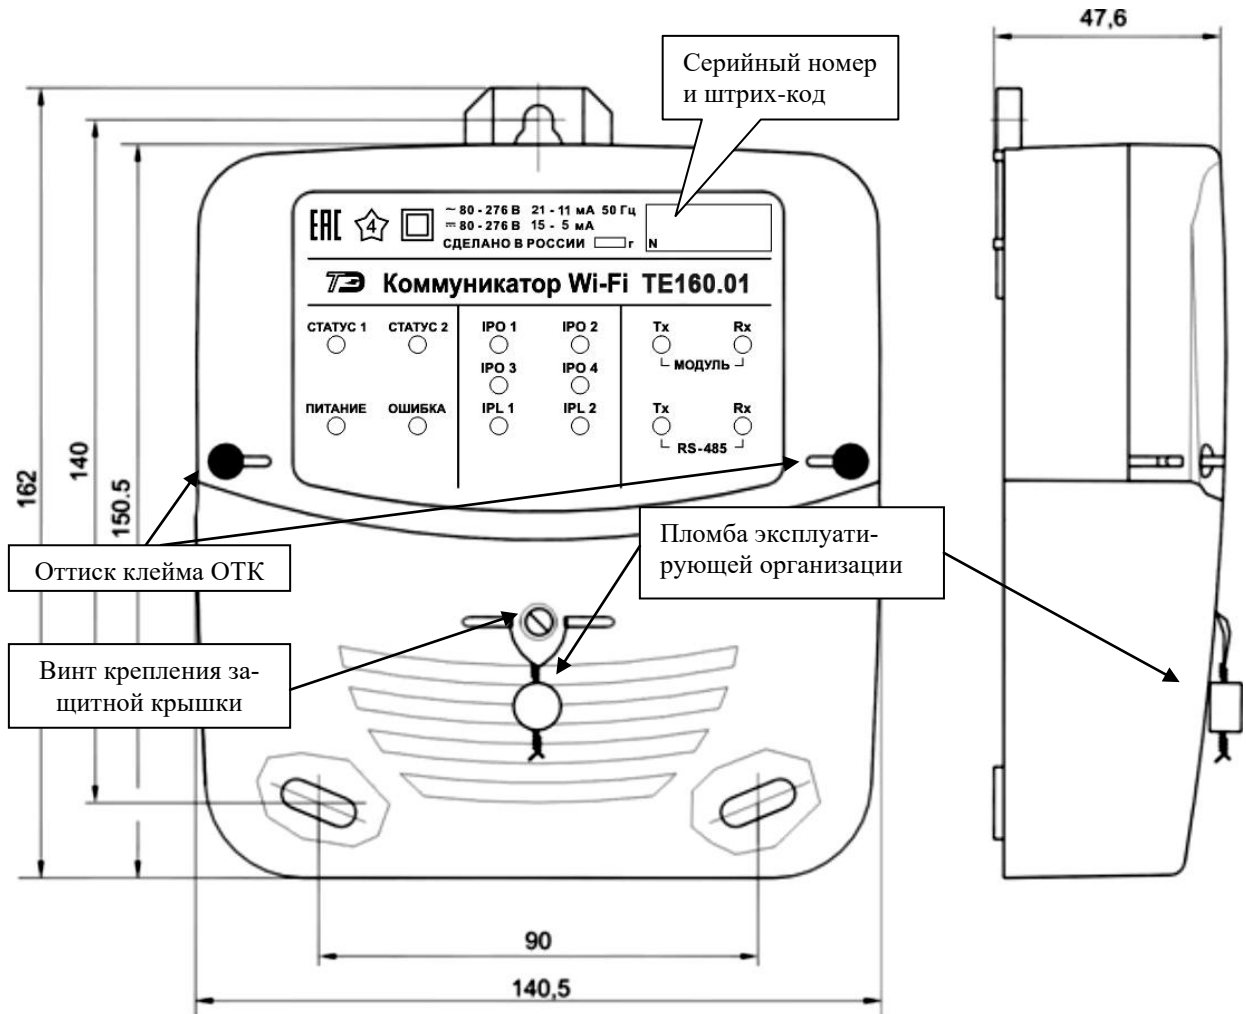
Габаритный чертеж и установочные размеры коммуникатора Wi-Fi TE160.01 с защитной крышкой
